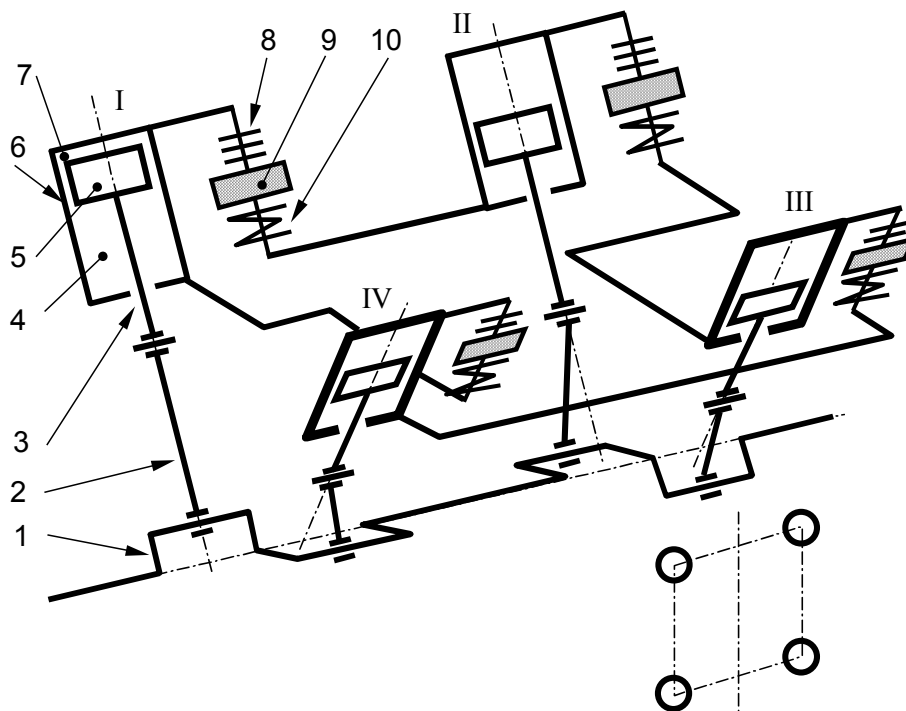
Motor Stirling cu pistoane cu dublă acțiune, cu cilindrii așezați în V și cu mecanisme bielă - manivelă: 1 - arbore cotit; 2 - bielă; 3 - tijă; 4 - cameră de comprimare; 5 - piston; 6 - cilindru; 7 - cameră de destindere; 8 - încălzitor; 9 - regenerador; 10 - răcitor
